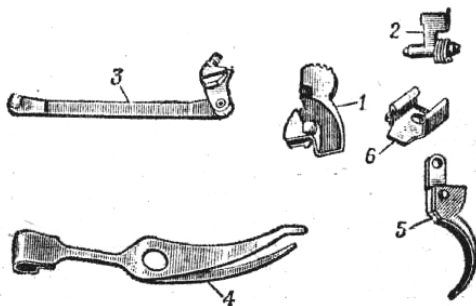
Части ударно-спускового механизма: 1 – курок; 2 – шептало с пружиной; 3 – спусковая тяга с рычагом взвода; 4 – боевая пружина; 5 – спусковой крючок; 6 – задвижка боевой пружины
